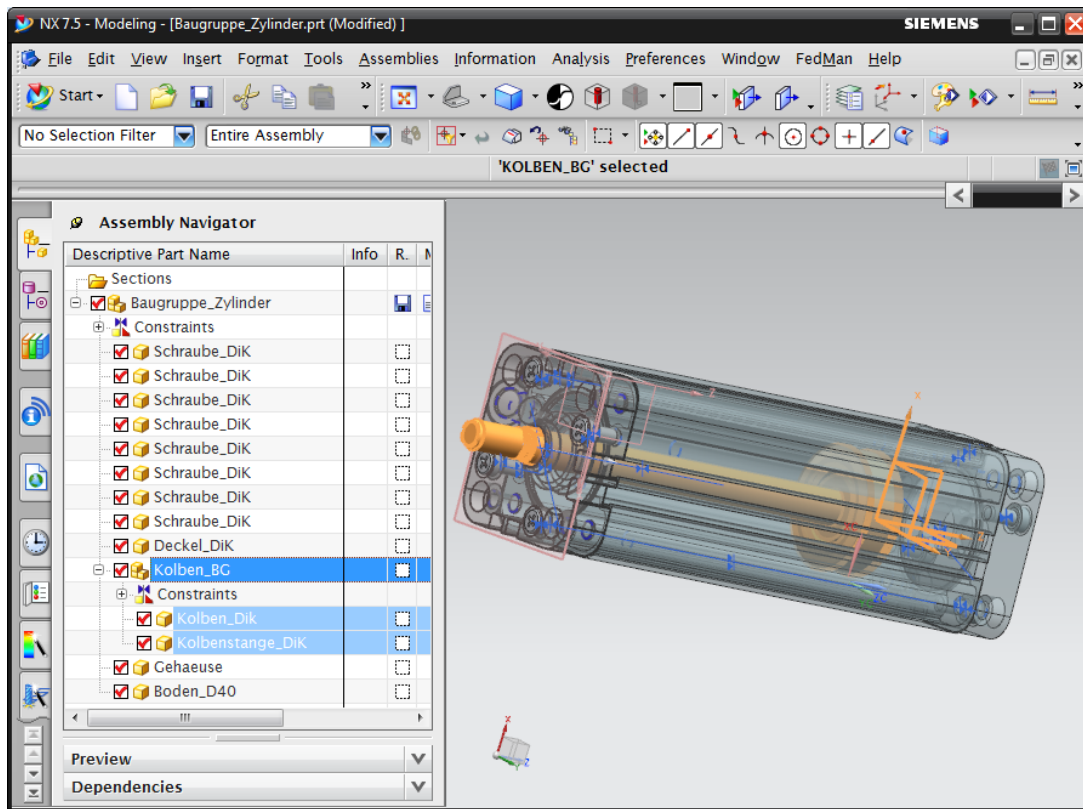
Conjunto montado e árvore de construção (subconjunto do eixo com eixo e êmbolo).
